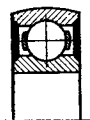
Шарикоподшипник со сферической поверхностью наружного кольца
